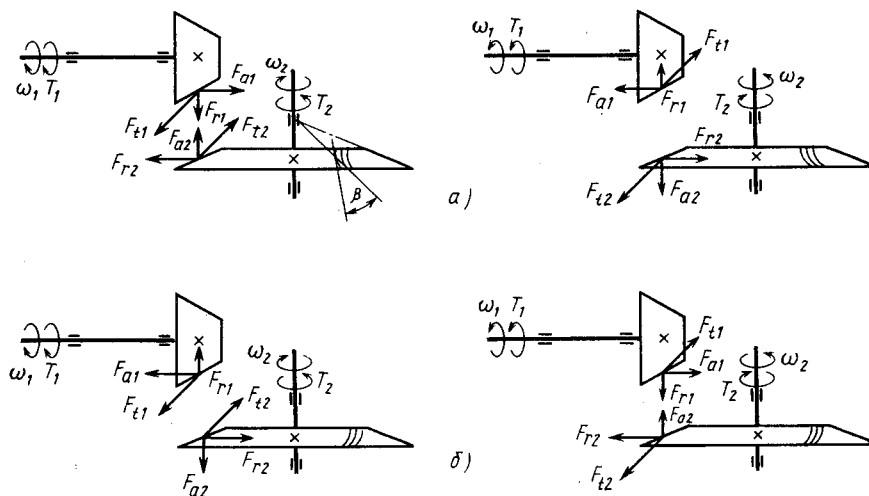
Схема сил в зацеплении конической передачи с круговым зубом и прямозубой: а — направление линии зуба колеса — левое, шестерни — правое; б — колеса — правое, шестерни — левое
